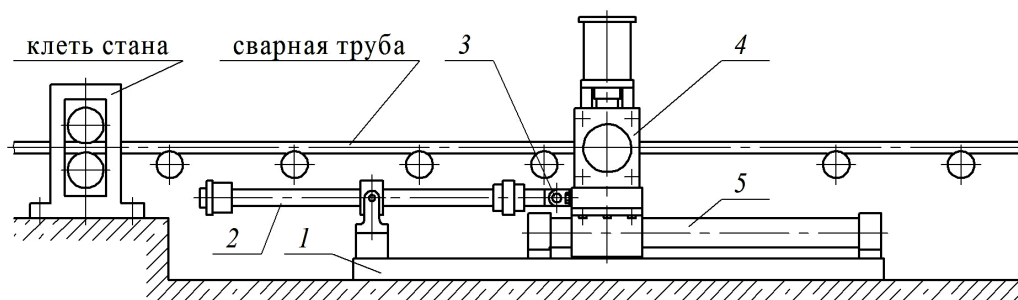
Структурная схема летучих ножниц трубосварочного стана
